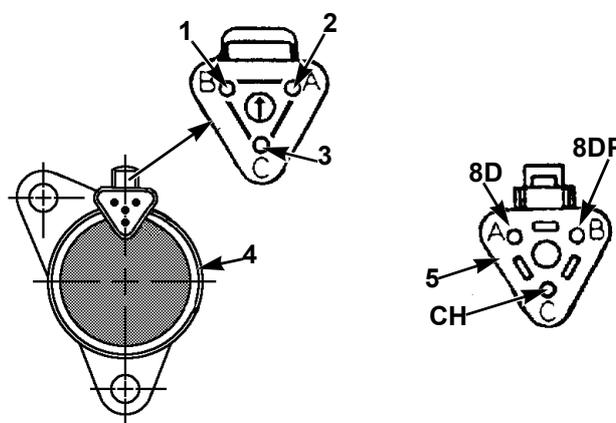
Регулировка скорости вращения двигателя для установок с опцией EcoPower
